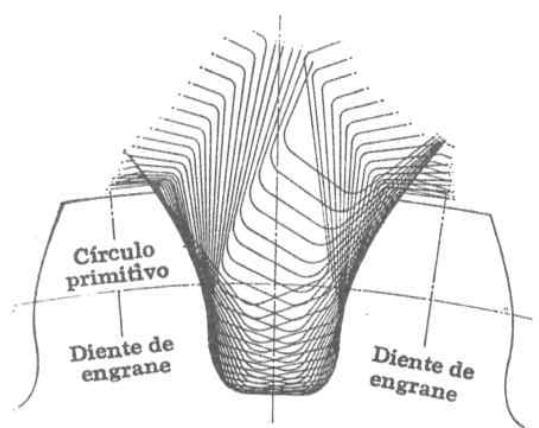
Movimiento coordinado y continuo entre la fresa madre y el engranaje
